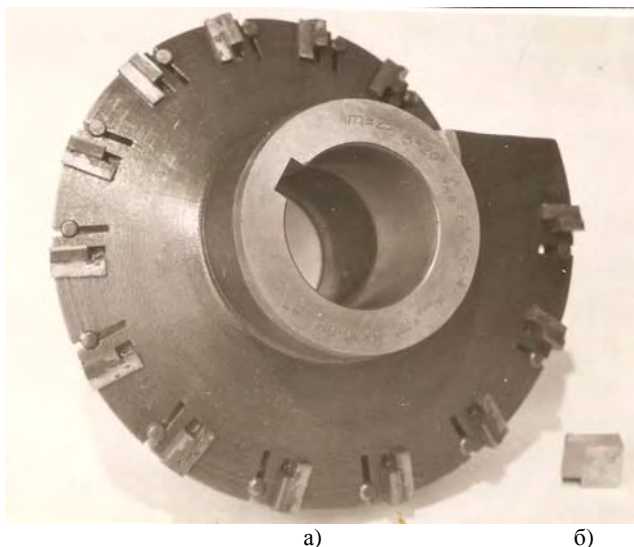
Рабочая конструкция левого корпуса двухкорпусной фрезы $m=25$ мм
